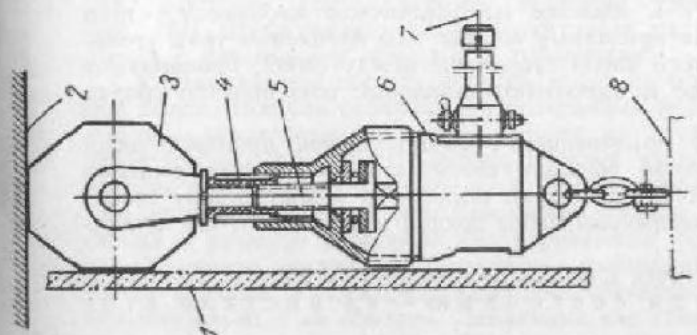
Пневмостяжка для механизации прижатия наружной обшивки к постели. 1 — постель; 2 — наружная обшивка; 3 — обшук; 4 — гайка; 5 — винт; 6 — ключ с импульсно-ударным механизмом; 7 — воздух из магистрала; 8 — стелд.
